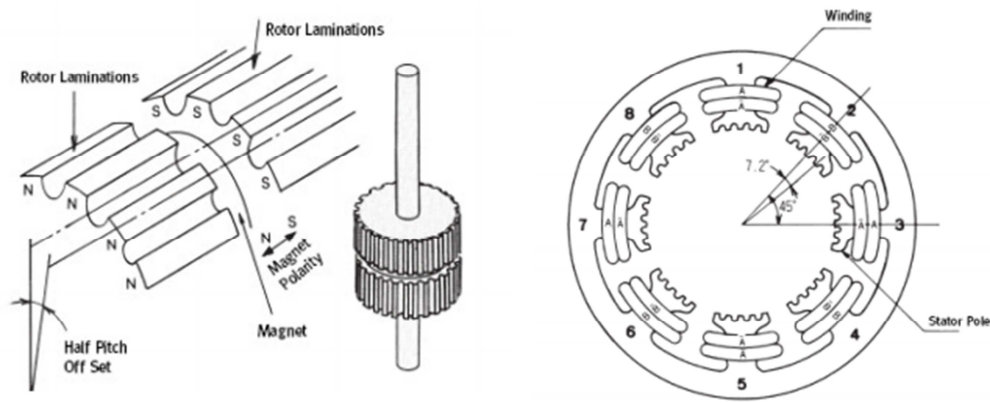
Vista detallada del rotor (esquerra) i de l'estator d'un motor pas a pas híbrid
